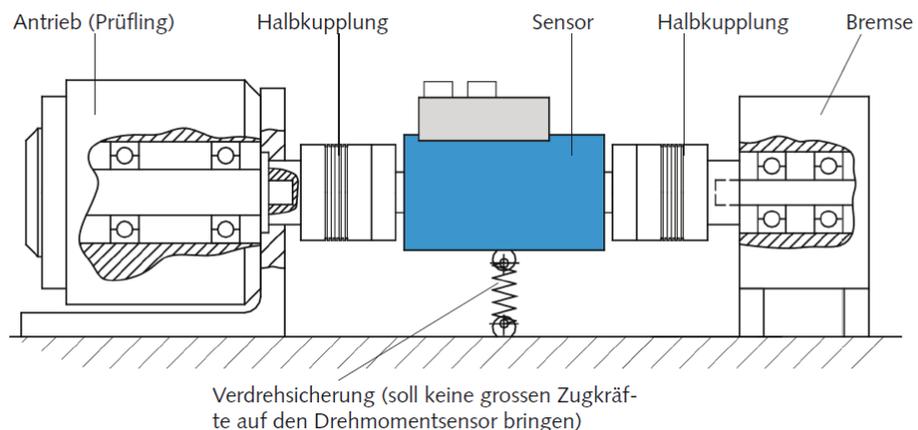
Einbau Sensor ohne Haltewinkel oder Gehäuseunterbau (GU)
